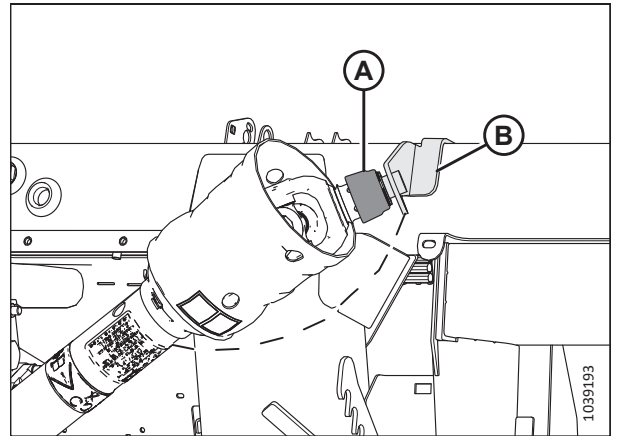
Приводний вал у положенні для зберігання — приводний вал Sidehill/Hillside B7180, B7181 або B7326
